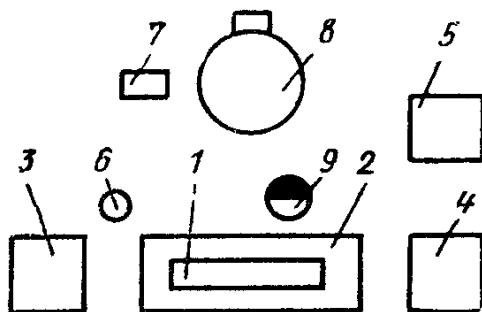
Схема организации рабочего места для отливки алюминиевых деталей с применением песчаных стержней:
